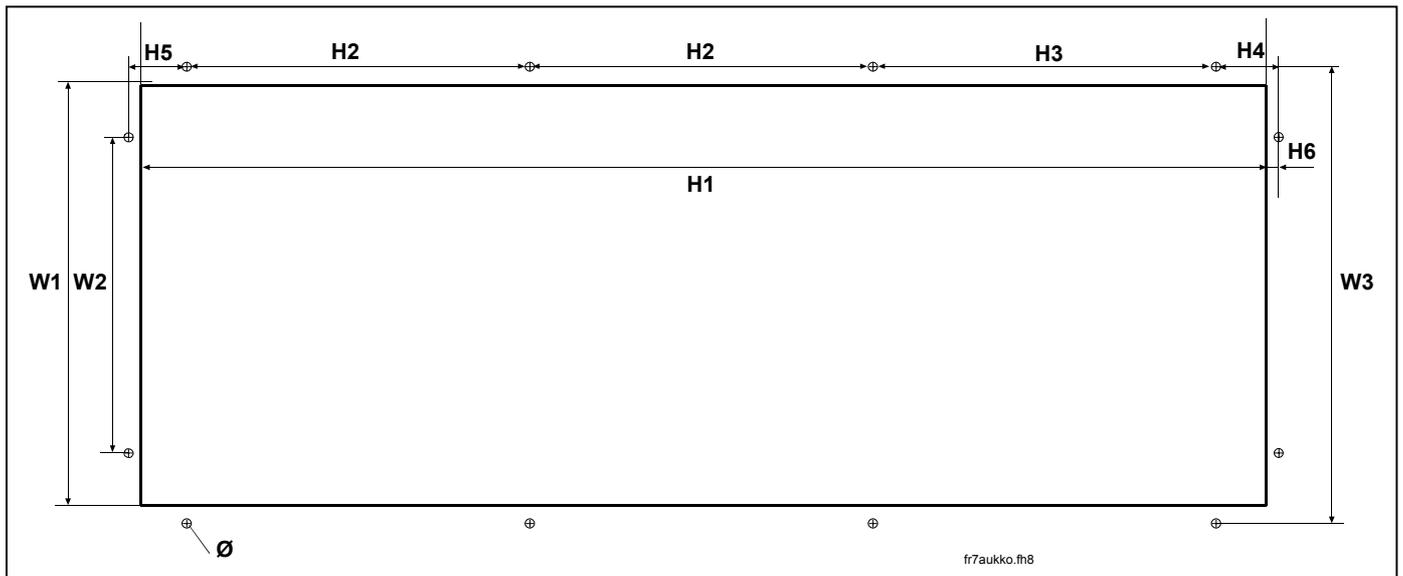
Разметка установочных отверстий для преобразователей частоты фланцевого исполнения габаритов FR7/R8
